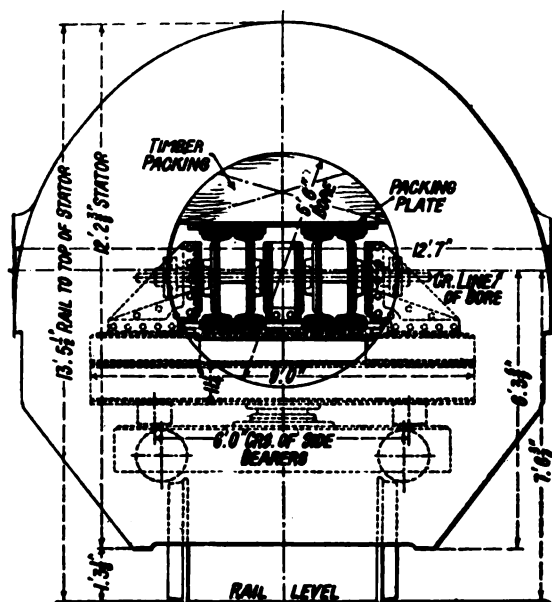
Sezione trasversale del carico e della trave longitudinale di sostegno.
